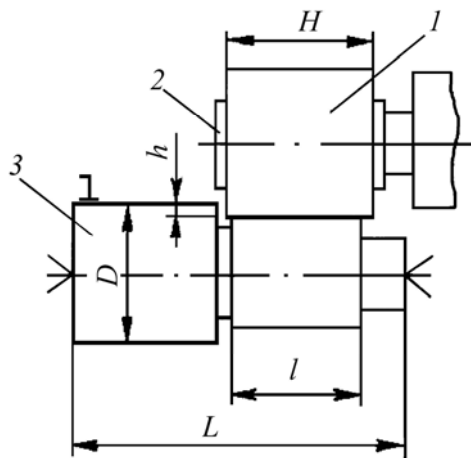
Схема установки заготовки детали на шлифовальном станке
